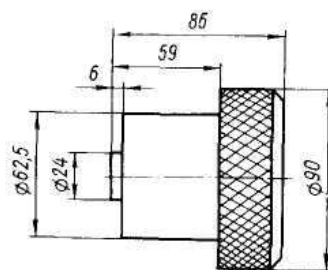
Оправка для запрессовки приводного вала в средний подшипник и зубчатого хвостовика с подшипником в сборе в кожух
